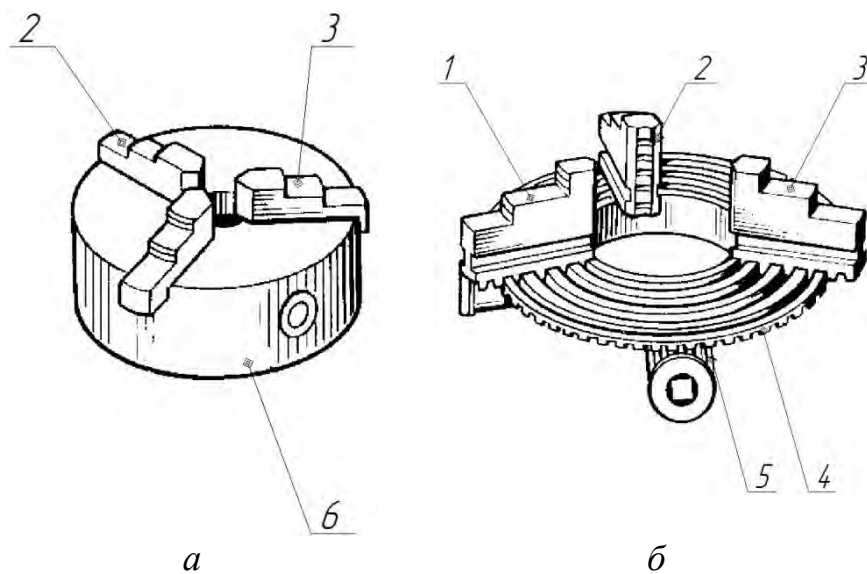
Трехкулачковый самоцентрирующийся патрон: 1, 2, 3, - установочно-зажимные элементы – кулачки; 4 – коническая шестерня со спиралью; 5 - приводное зубчатое колесо; 6 - корпус
